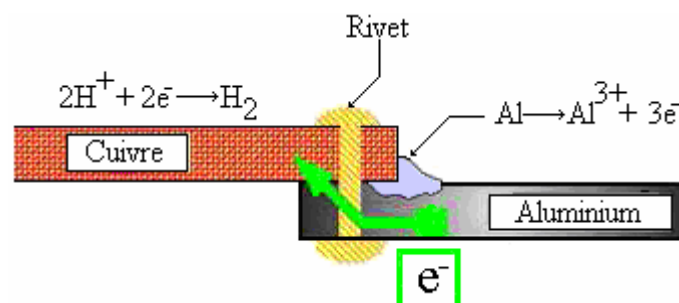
Exemple de corrosion galvanique pour un assemblage de tôles aluminium et cuivre par un rivet sans isolation.
